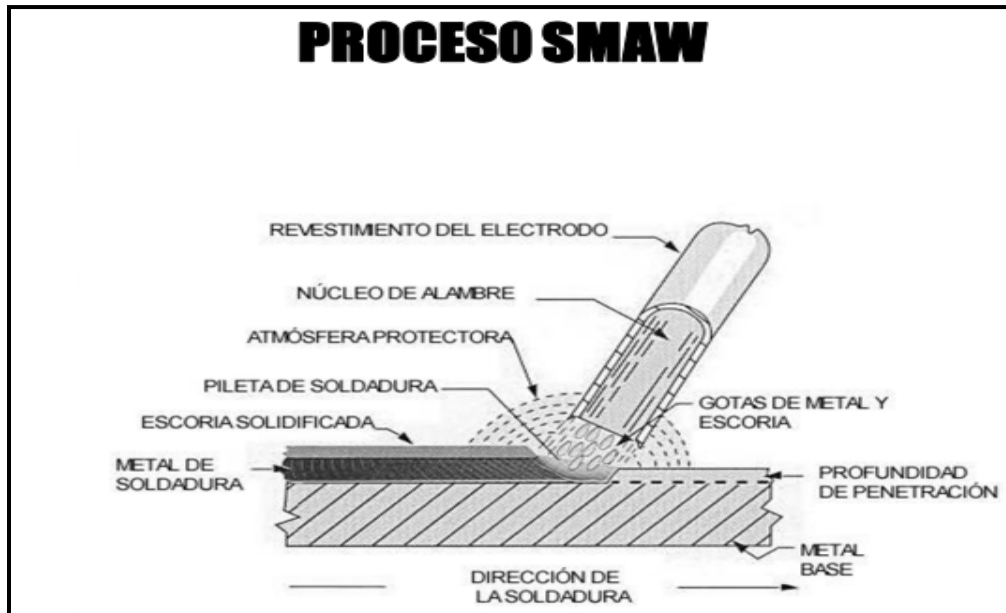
Proceso de soldadura (SMAW)
